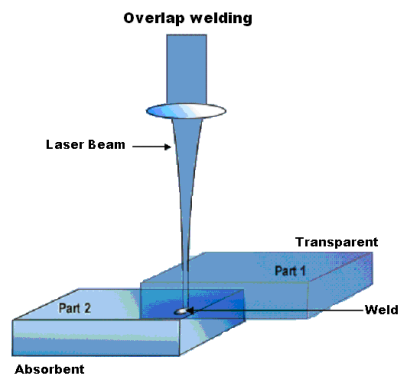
Rappresentazione schematica del processo “laser welding”
